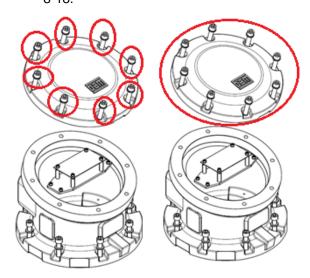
Демонтаж крышки клеммной коробки
